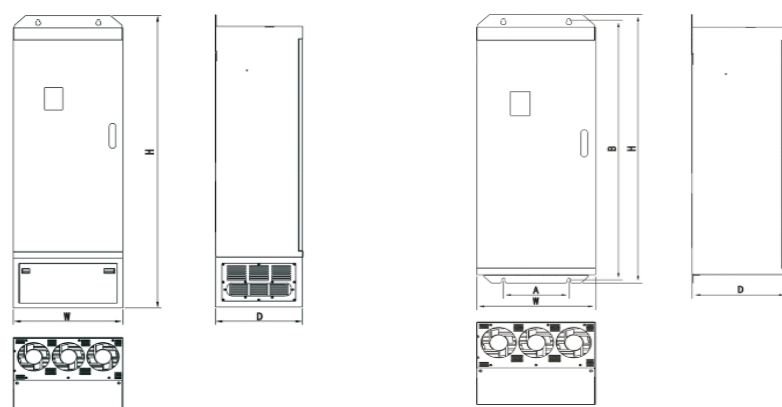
Габаритные размеры (185-315кВт, с базой и без базы)
